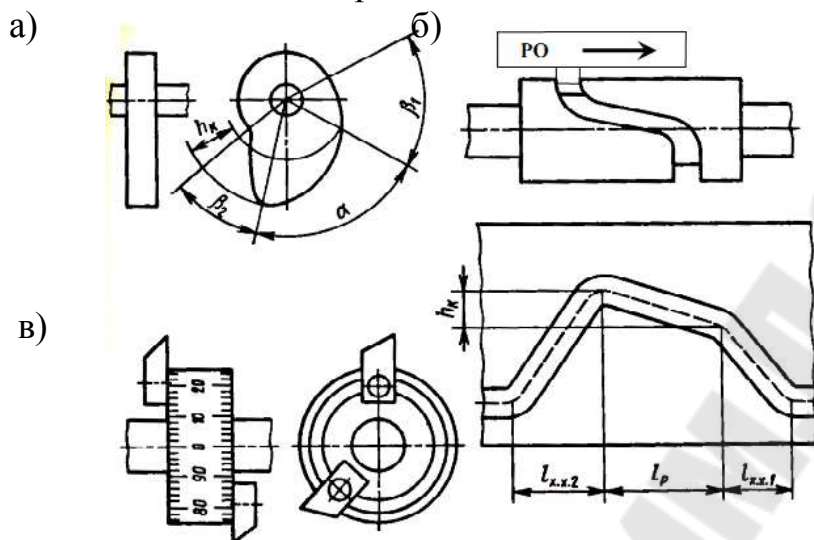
Кулачки, устанавливаемые на распределительный вал: а- дисковый; б- цилиндрический (барабанный) и его развертка; в – командный
